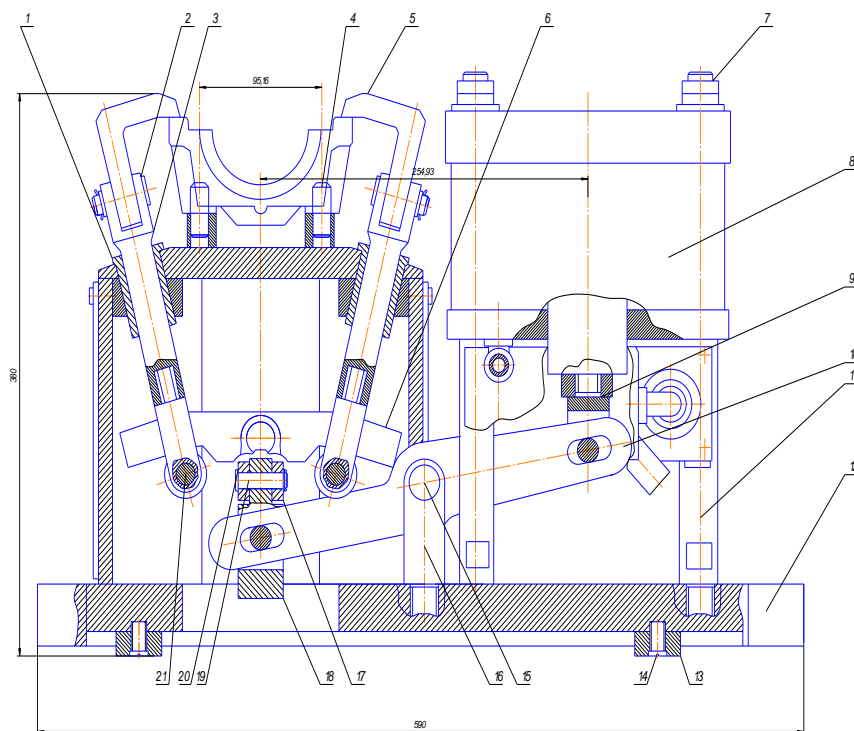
Общий вид устройства устройства для фрезерования крышек шатунов: 1 - рама; 2 - шток; 3 - втулка; 4 - фиксатор; 5 - крюк; 6-рычаг; 7 - гайка; 8 - пневмоцилиндр; 9- шток; 10- рычаг; 11-шпилька; 12-плита; 13 - фиксатор; 14 - винт; 15 - палец; 16 - кронштейн; 17 - втулка; 18 - кронштейн; 19-палец; 20-штифт; 21 - палец.
